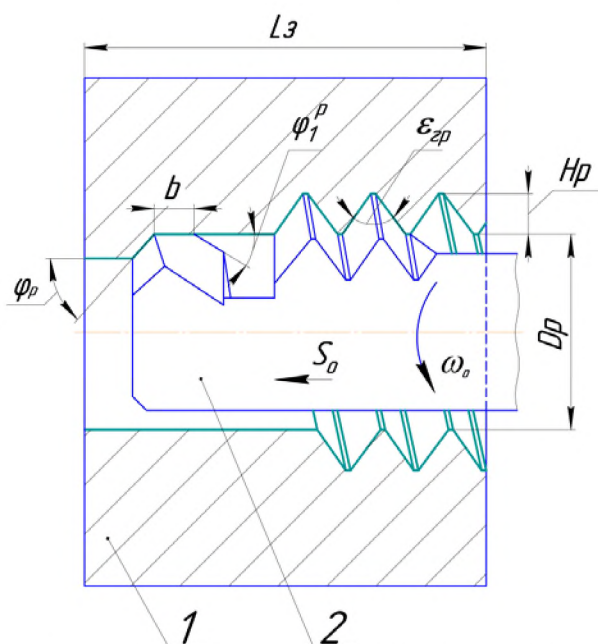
Схема нарезания внутренней резьбы комбинированным инструментом резцом-гребёнкой
